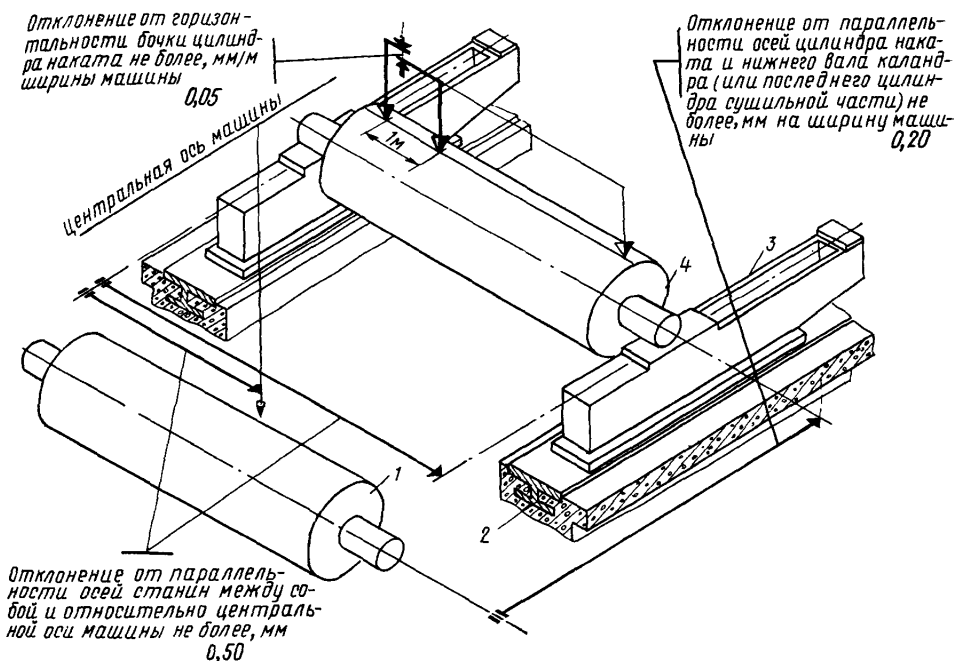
Схема, основные контролируемые монтажно-установочные размеры и допуски на монтаж наката:
